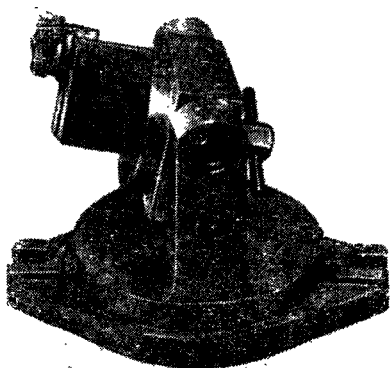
Приспособление для заточки гребенок по передней поверхности
